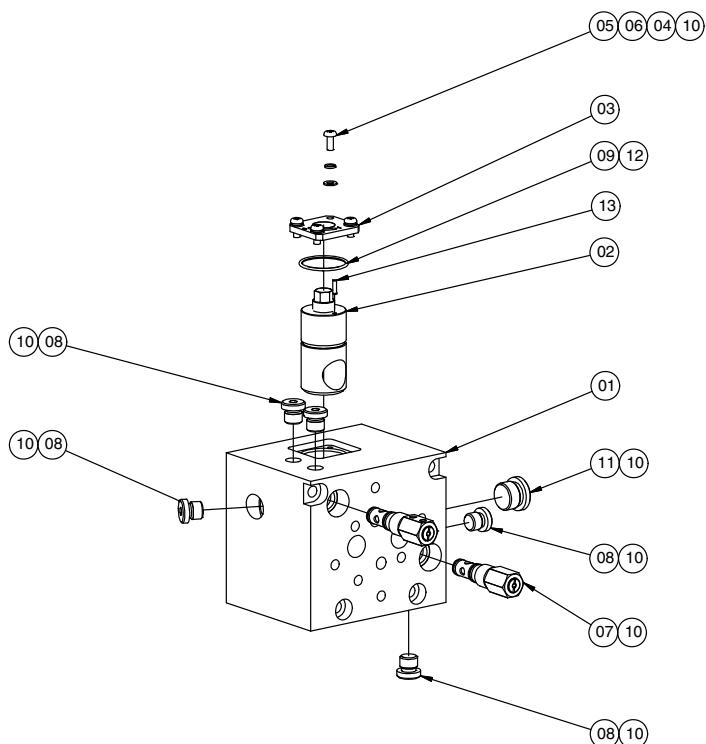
Peças para adaptador de bomba de caudal duplo
